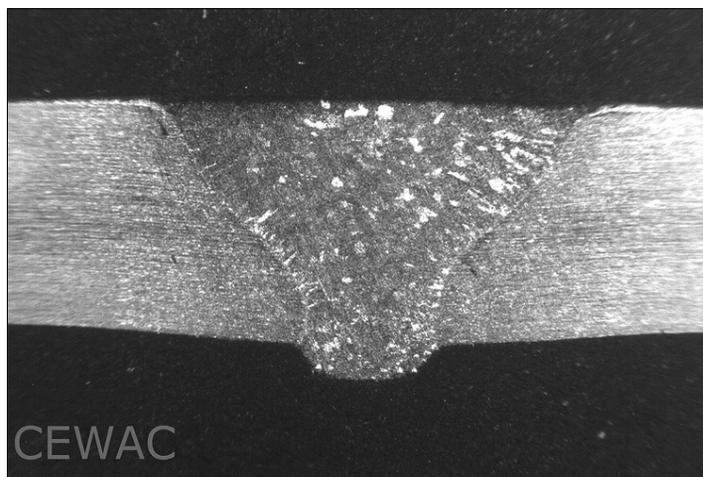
soudure HLW bout-à-bout d'aluminium série 7xxx (3 mm) à 2,3 m/min
